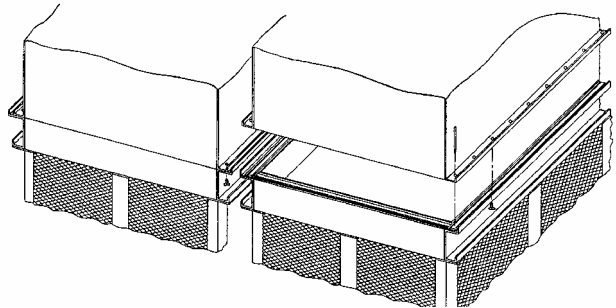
Emparejamiento de las Secciones Superiores Sobre las Secciones de Bandeja
